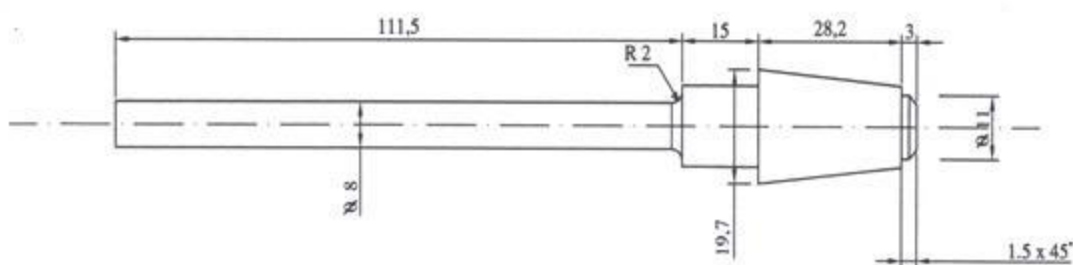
Éprouvette d'essai de fatigue la machine GUNT WP 140.
